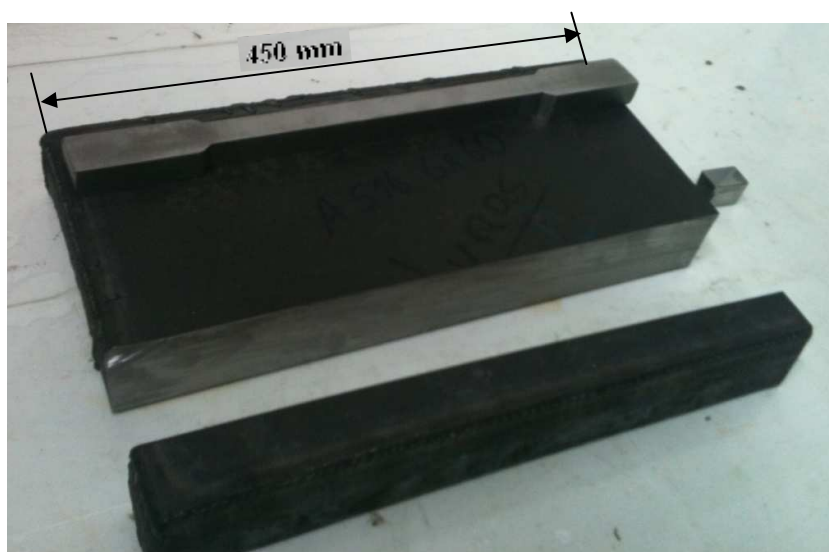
Material bruto e corpo de prova para ensaio de tração
